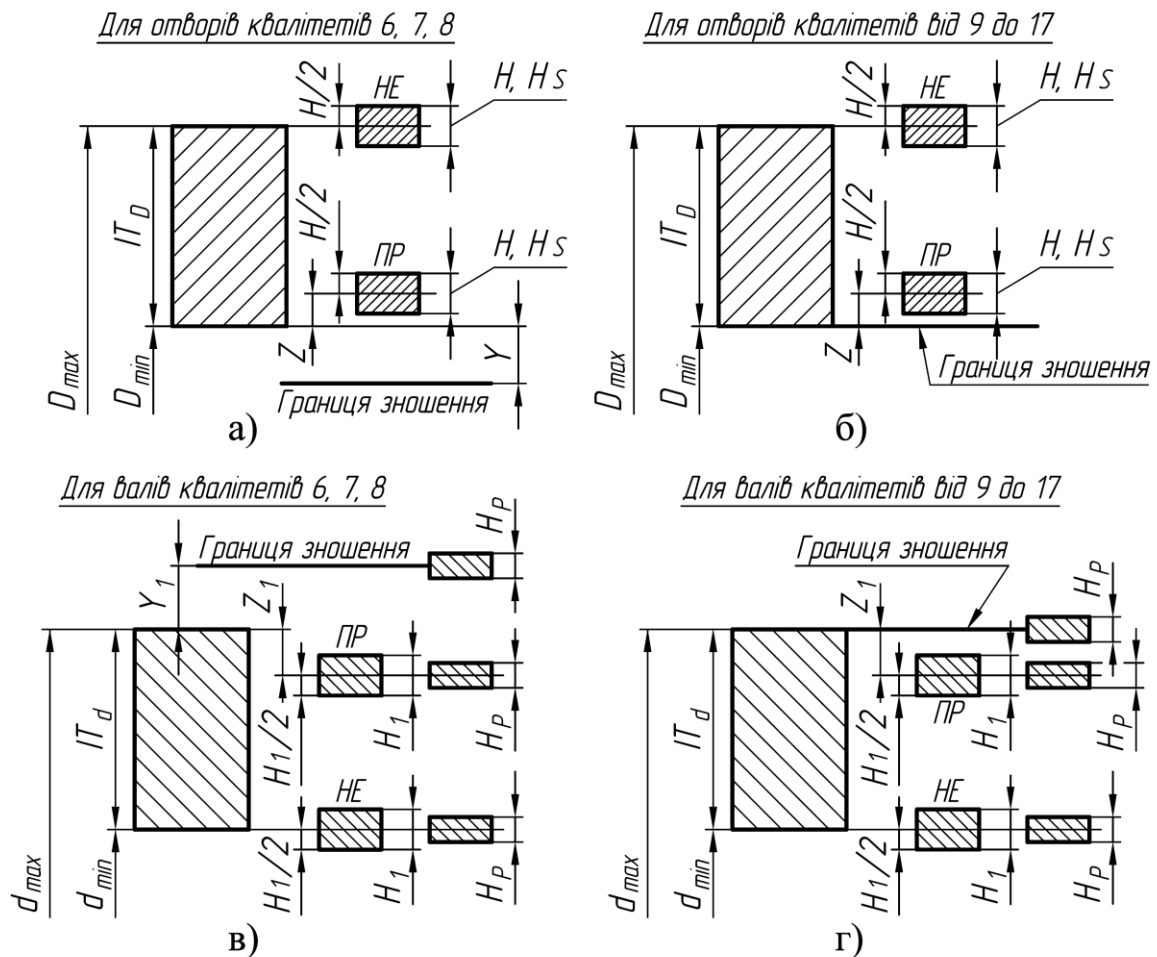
Схема розміщення полів допусків калібрів для номінальних розмірів до 180 мм. а), б) - схеми полів допусків калібру-пробки; в), г) - схеми полів допусків калібру-скоби:
